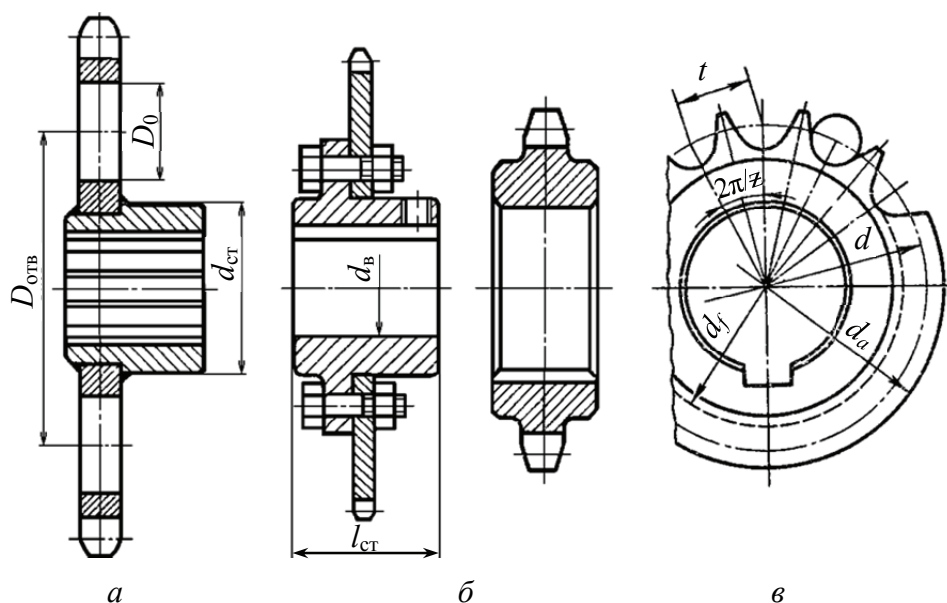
Конструкции звездочек для роликовых и втулочных цепей:
